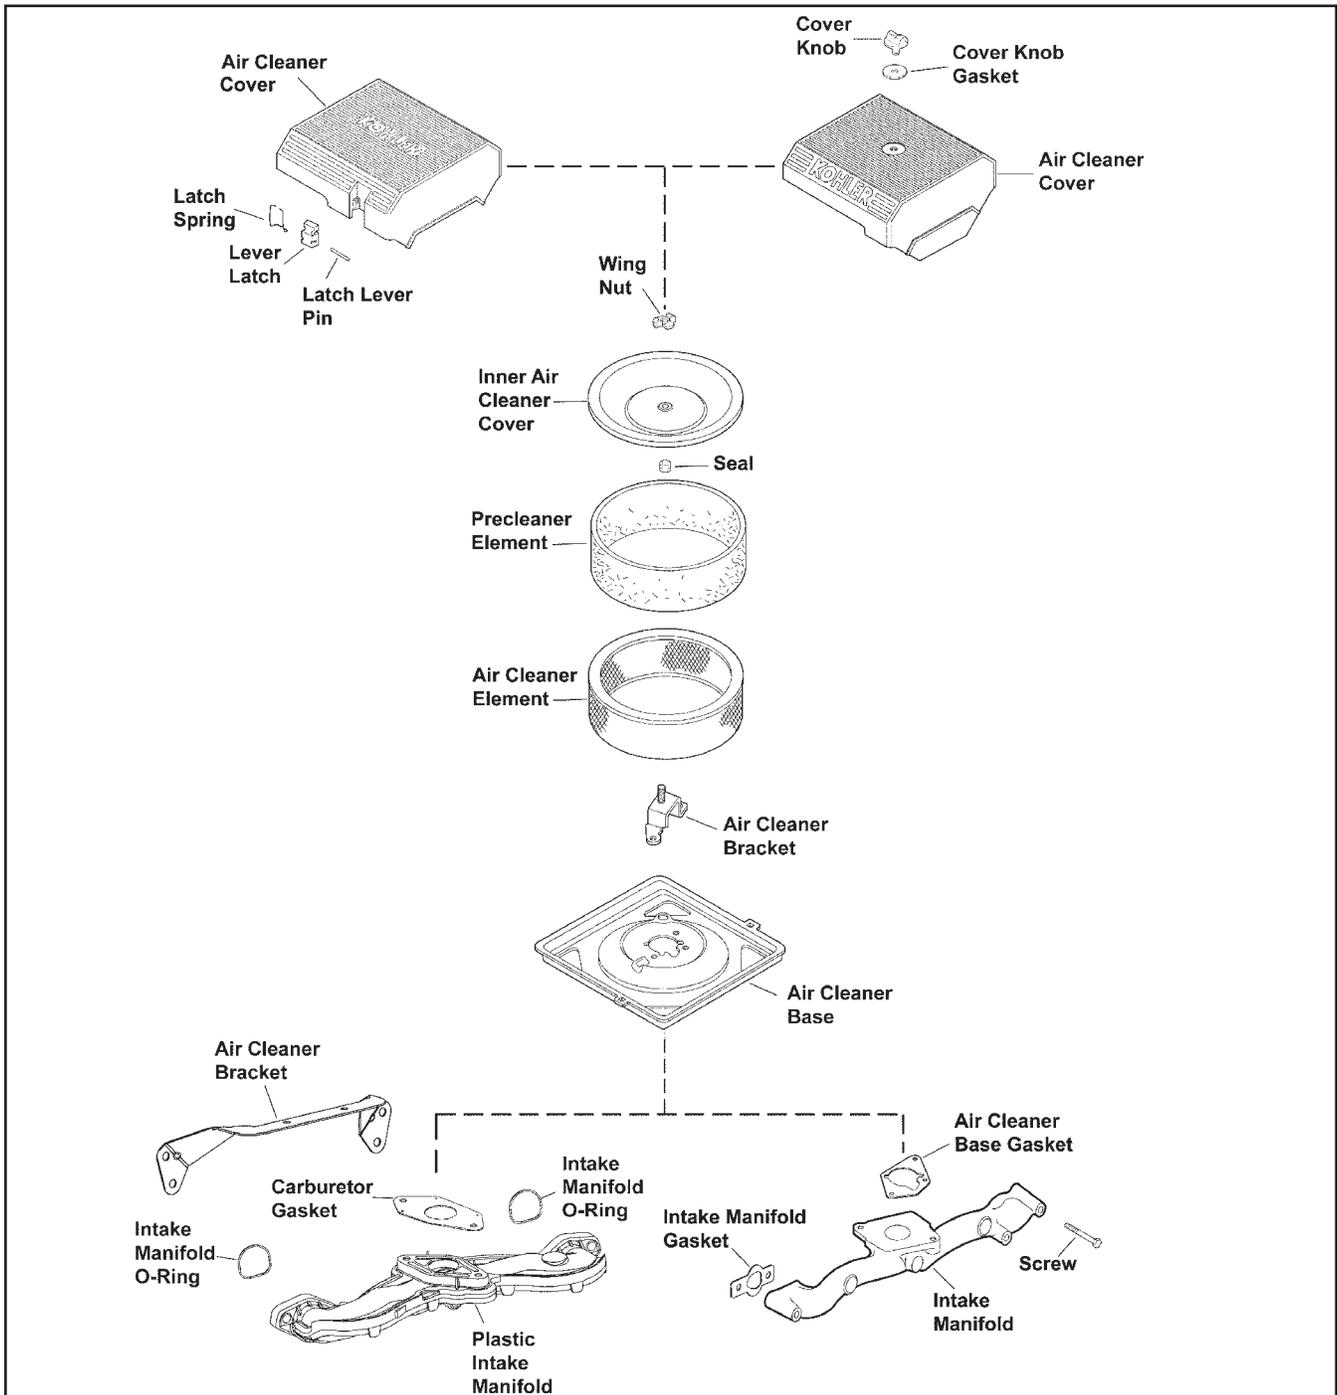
Explosionszeichnung der Teile des Standard-Luftansaugsystems.
